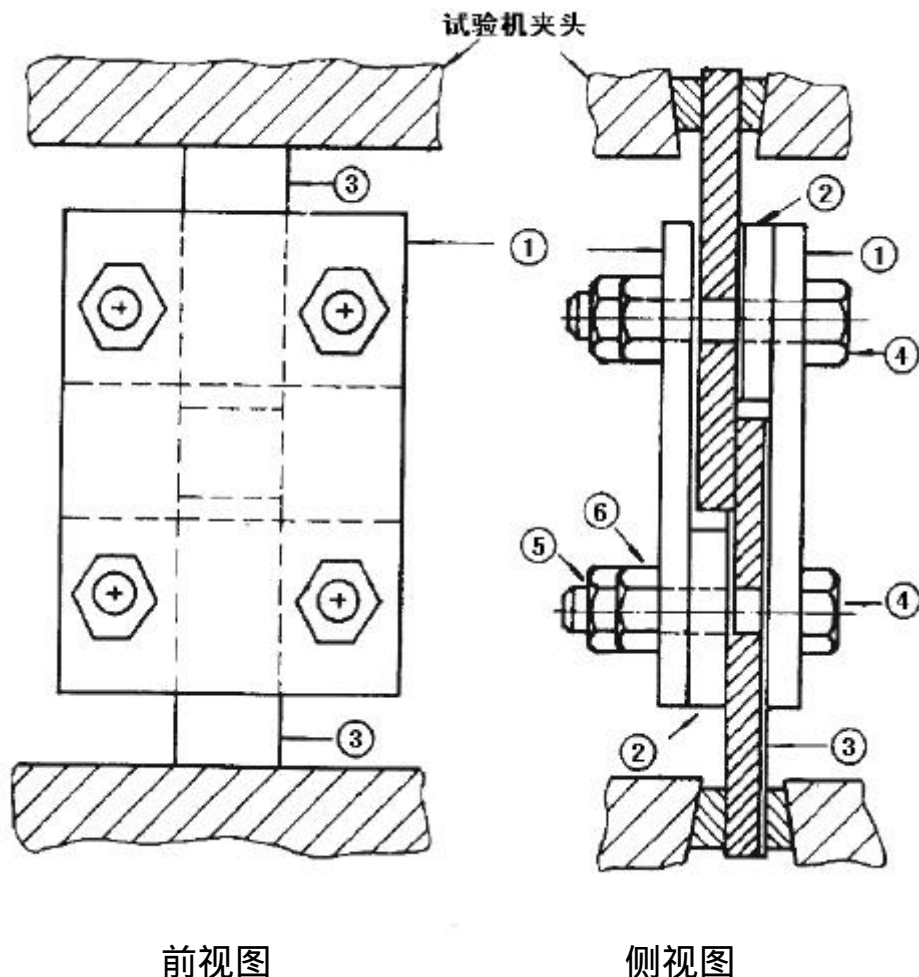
钎焊接头拉伸试验用卡具
